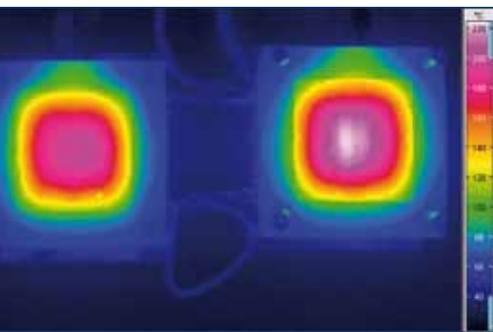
Beidseitig induktiv beheiztes Werkzeug (Werkzeug geöffnet)
